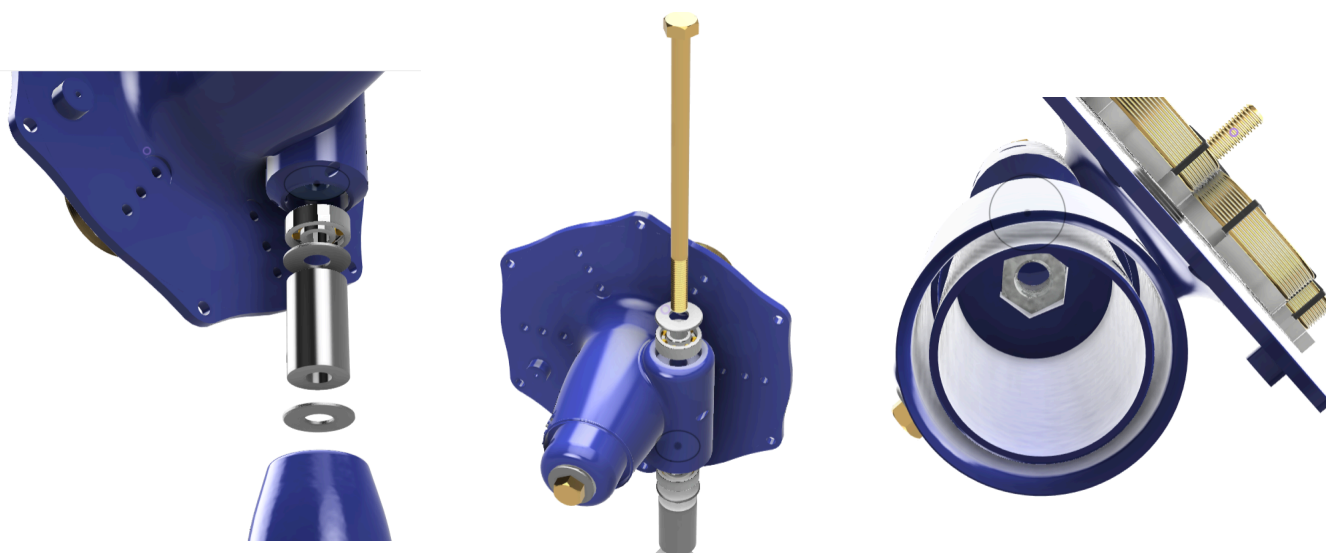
Vistas del montaje del cabezal con su mecanismo de pivotaje.
